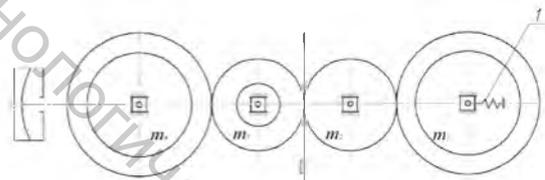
Четырехвальный отжим с упругой установкой опорного вала
